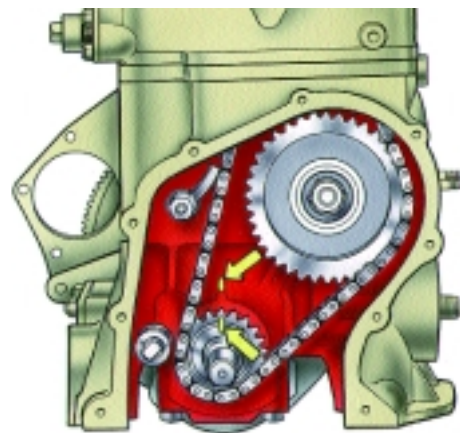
Проверка совпадения установочной метки на звездочке коленчатого вала с меткой на блоке цилиндров двигателя мод. 2106-70
